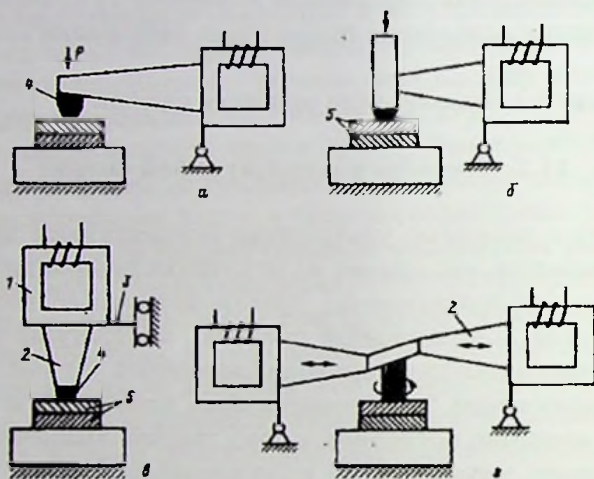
Схема типовых колебательных систем для ультразвуковой сварки металлов:
